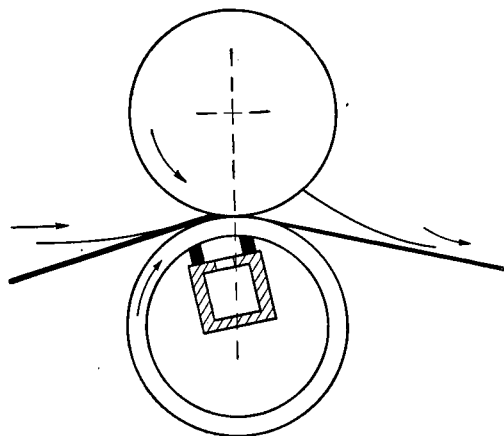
Положение вакуум-камеры в отсасывающем прессовом валу
